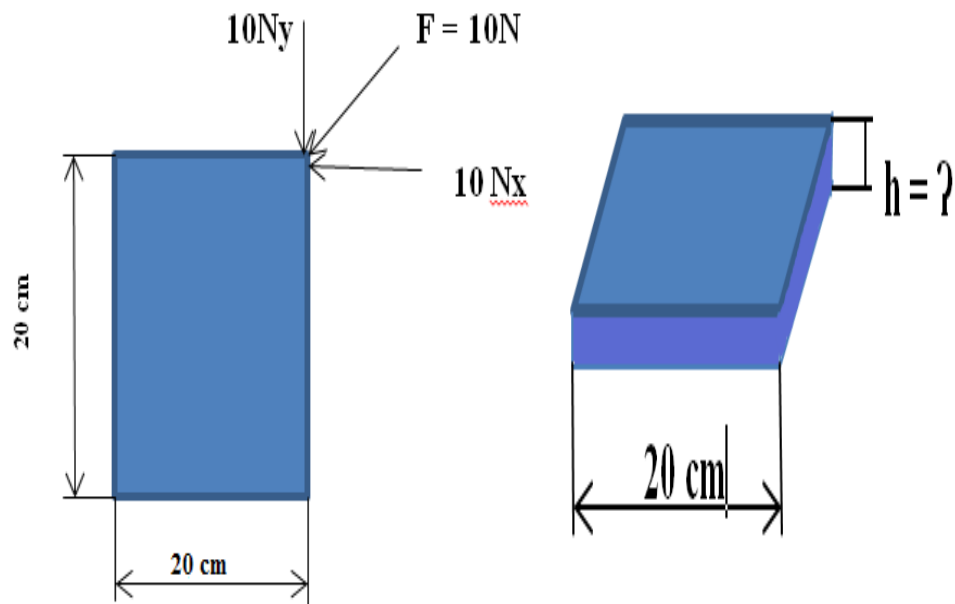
Fuerzas que actúan sobre la placa que soporta el motor de arranque y espesor a calcular
